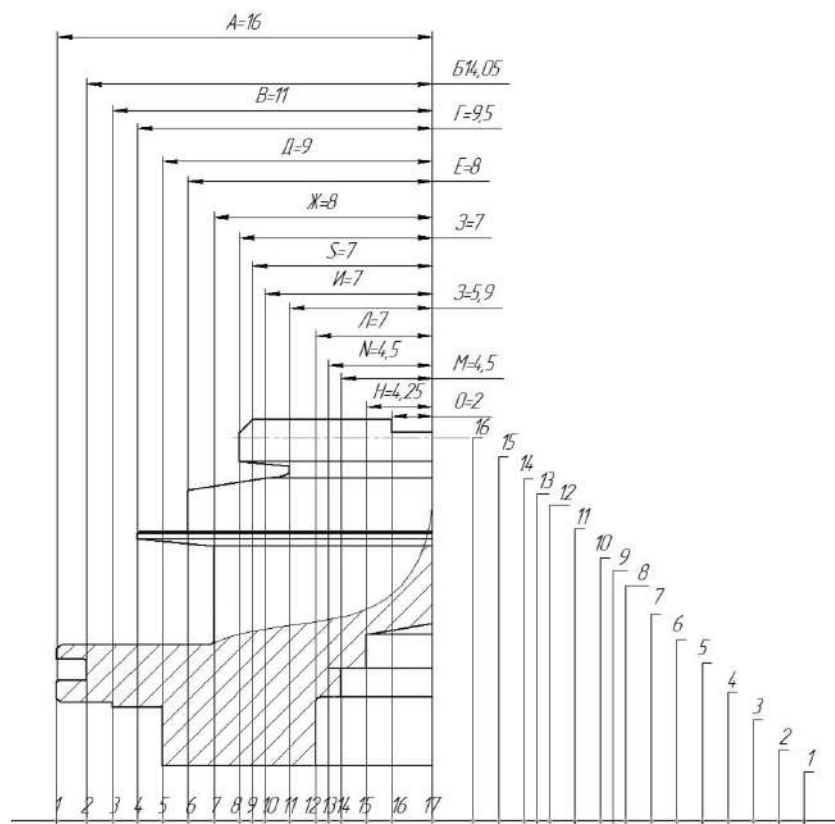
Преобразованный чертёж детали во второй проекции
